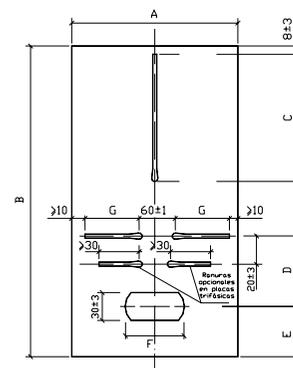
Dimensiones de las placas de montaje de contadores en centralizaciones tipo panel
